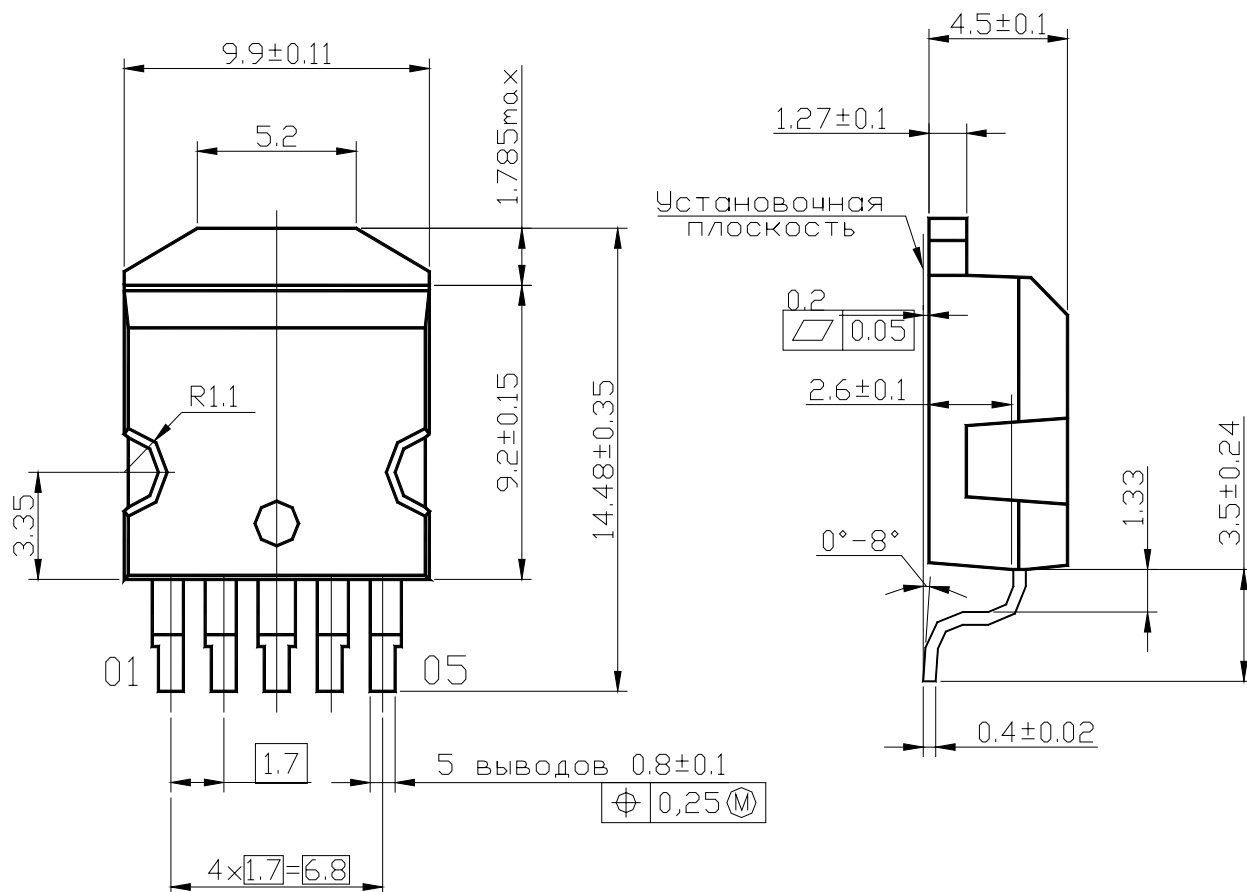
Габаритный чертеж корпуса 1501Ю.5-А
